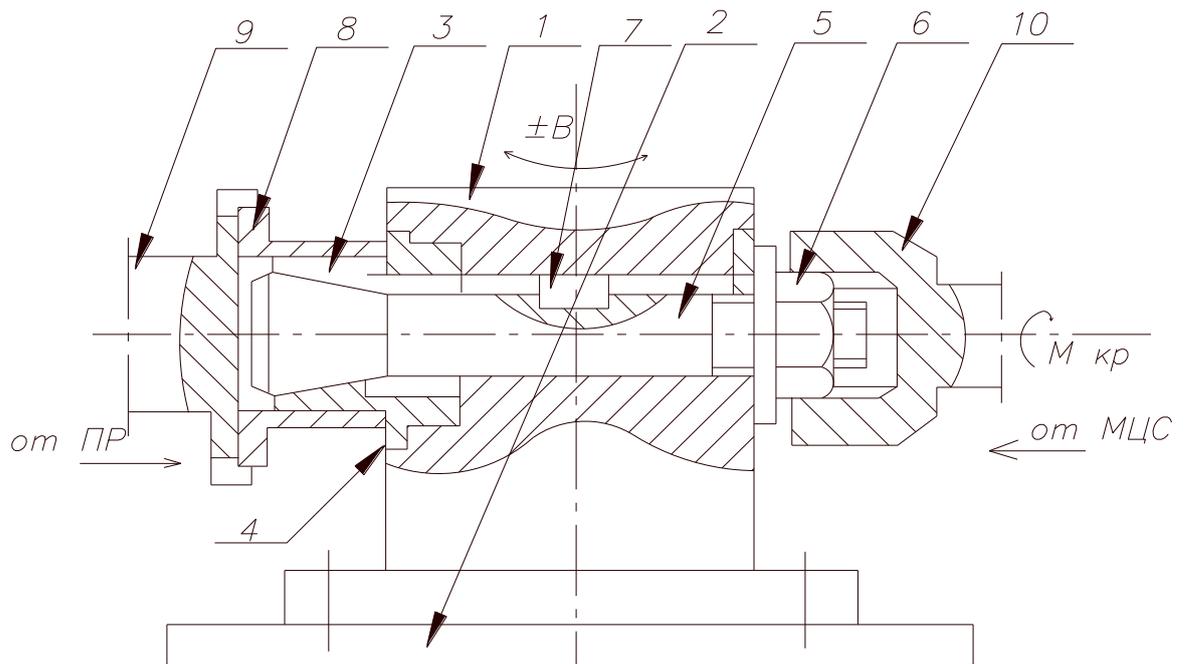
Схема взаимодействия оправки-ключа (10) и ПР (9) при автоматической установке и закреплении заготовки в многоцелевом станке
